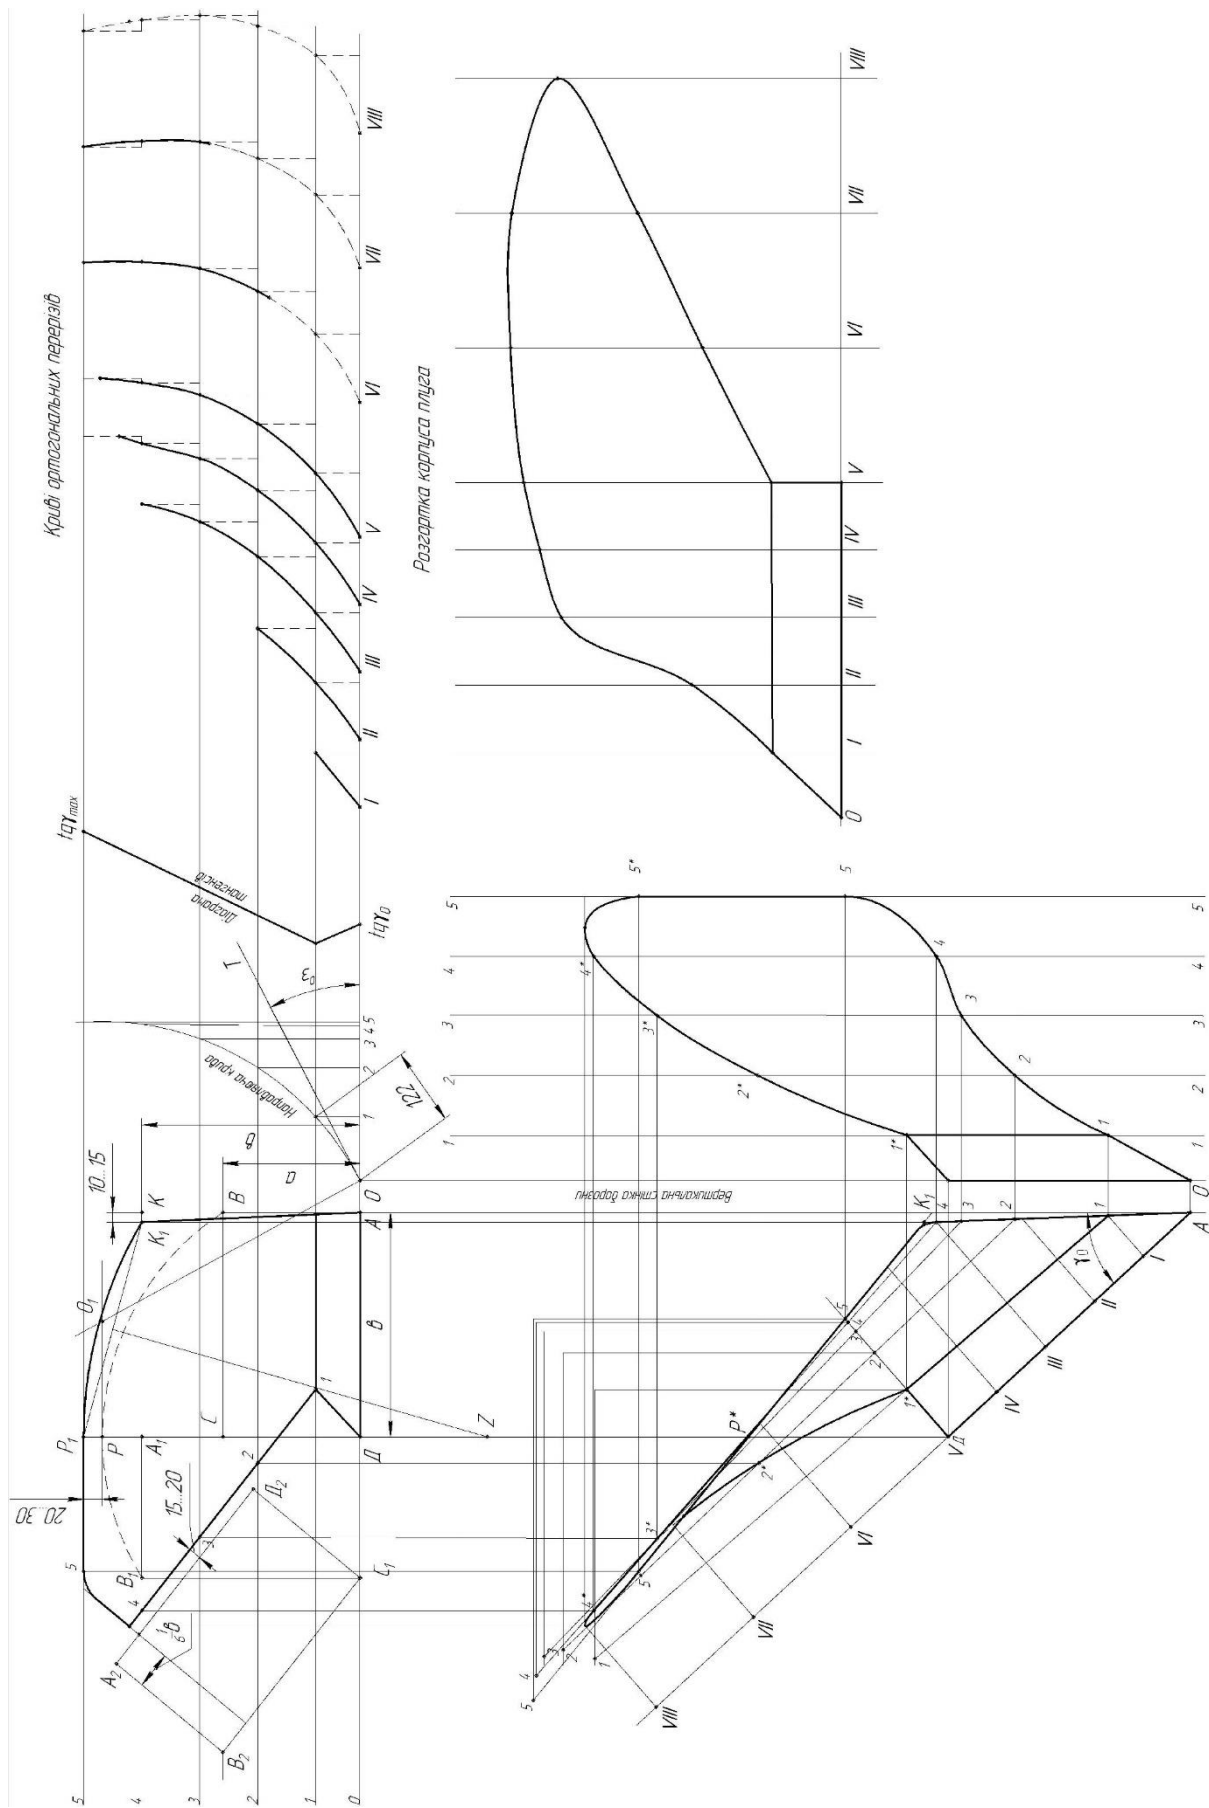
Загальний вигляд спроектованої робочої циліндроїдальної поверхні корпусу плуга
